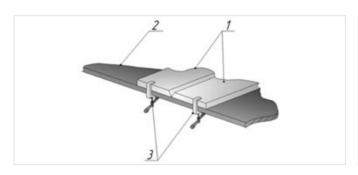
Схема сборки пластин исследований режимов полуавтоматической сварки.
